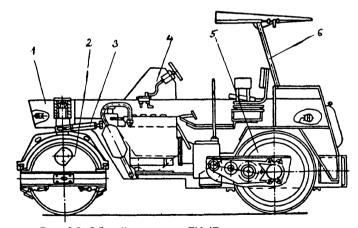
Общий вид катка ДУ-47: 1 - рама; 2 - направляющий валец; 3 - гидроцилиндр рулевого управления; 4 - пульт управления; 5 - вибровалец; 6 - тент
